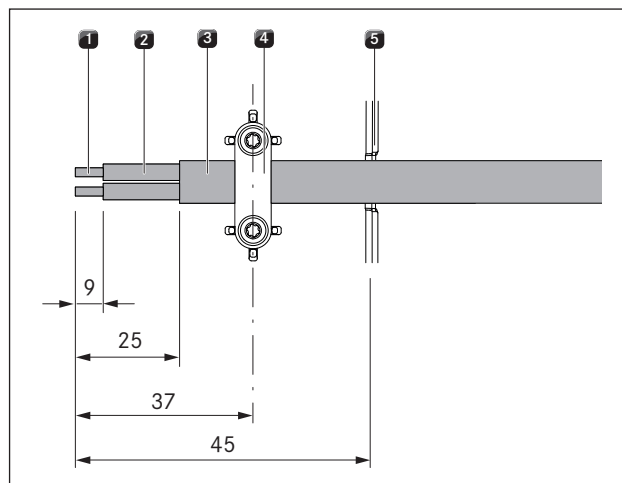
Lunghezze di isolamento e posizione di montaggio del cavo di collegamento
